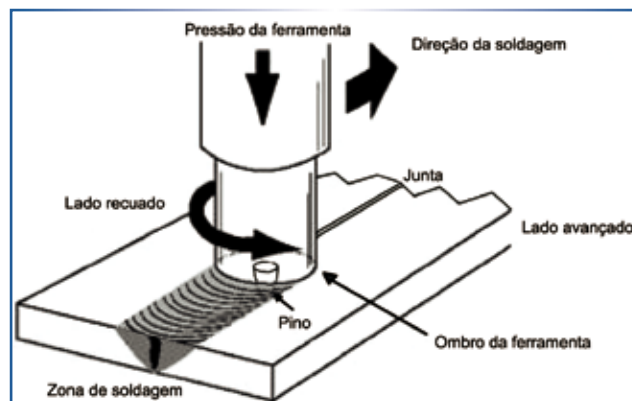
Processo de união entre duas chapas usando soldagem por fricção linear⁽⁶⁾
